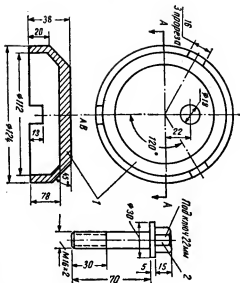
Приспособление для проверки зазора в роликовых подшипниках:
